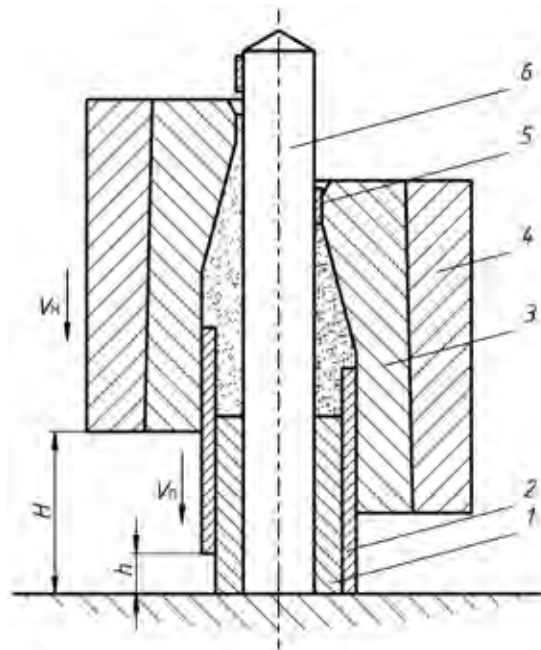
Схема и перемещения элементов лабораторного штампа для формирования детали со сдвигами слоев порошка
